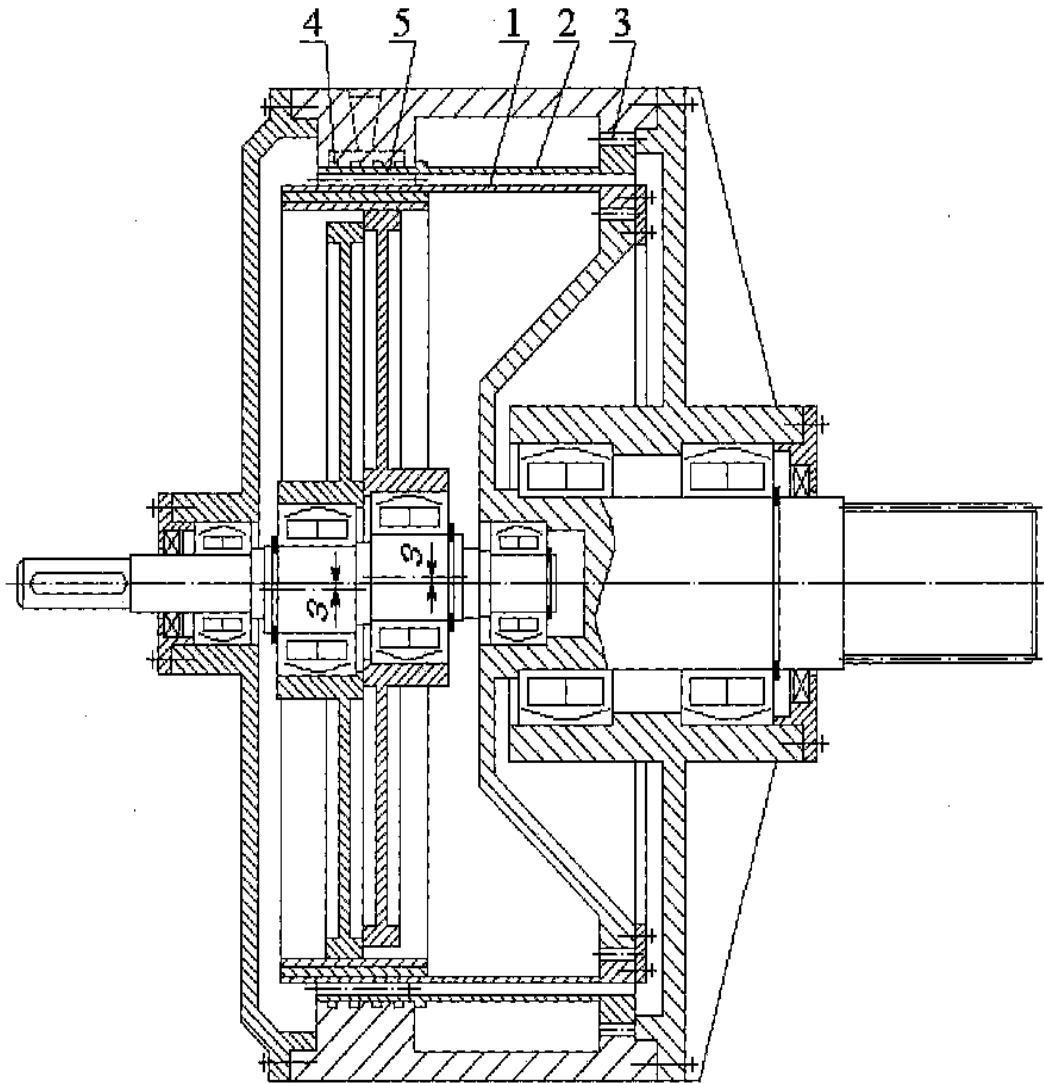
Хвильовий зубчастий редуктор з двома гнучкими колесами
